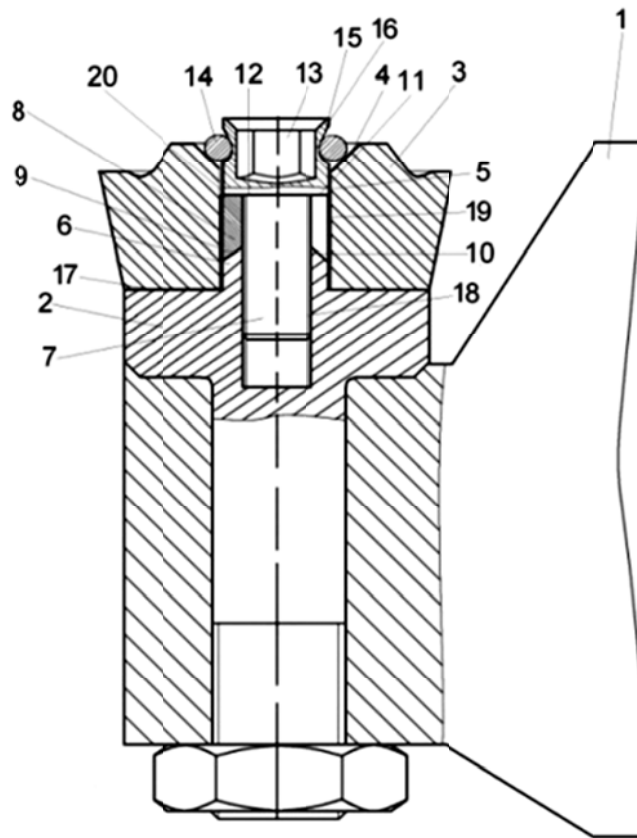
Усовершенствованная конструкция сборного чашечного резца
